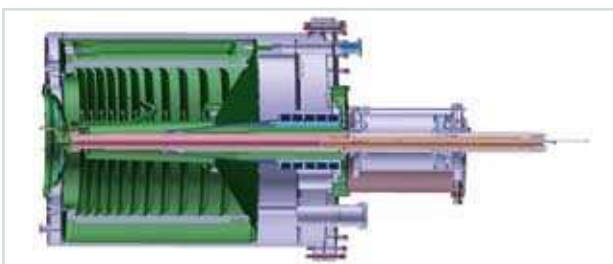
3D-CAD-Modell der Prototyp-Toruskryopumpe. Das Einlassventil (links) hat einen Durchmesser von 800 mm.
